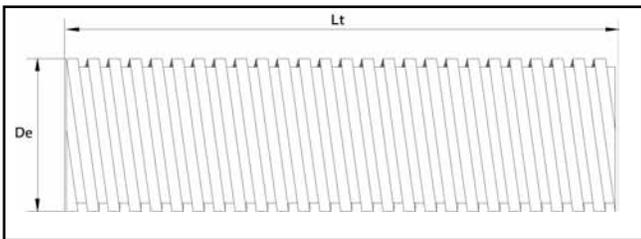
Tubería de pared estructurada de perfil abierto helicoidal
